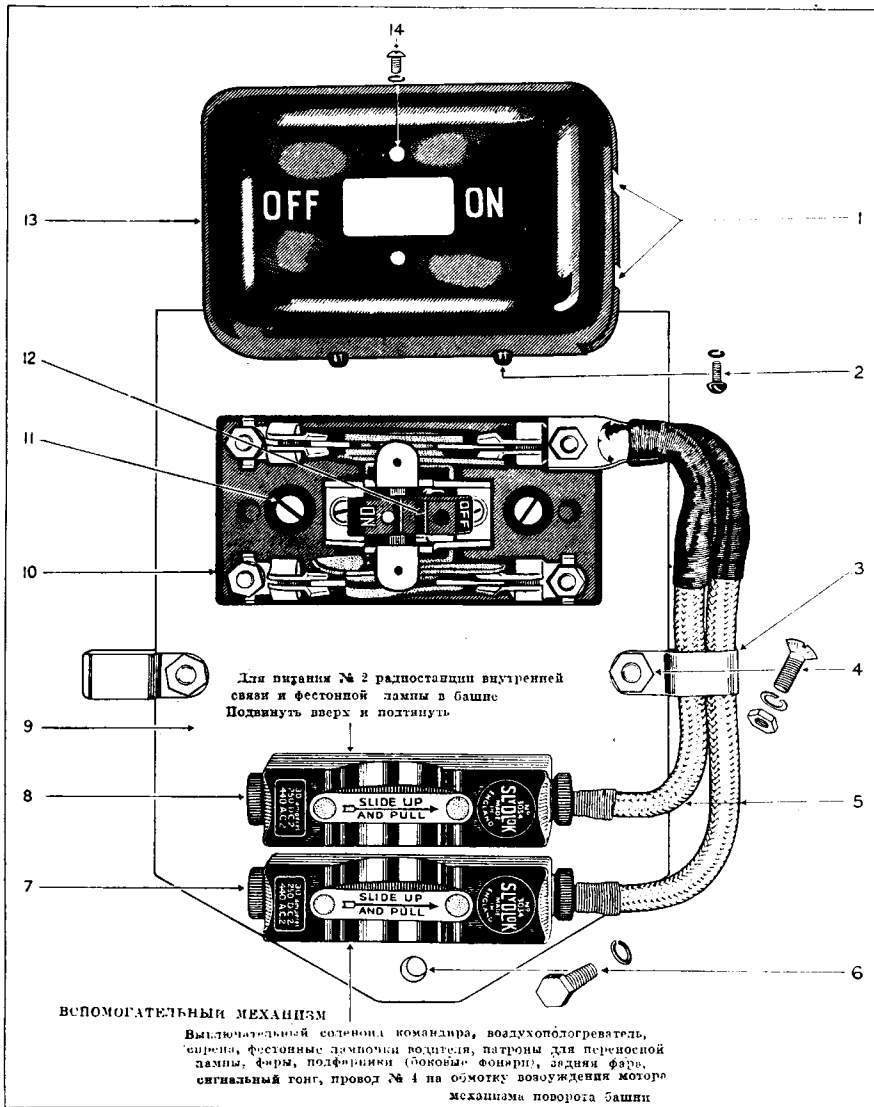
Главный переключатель (электрооборудование корпуса в сборке).
